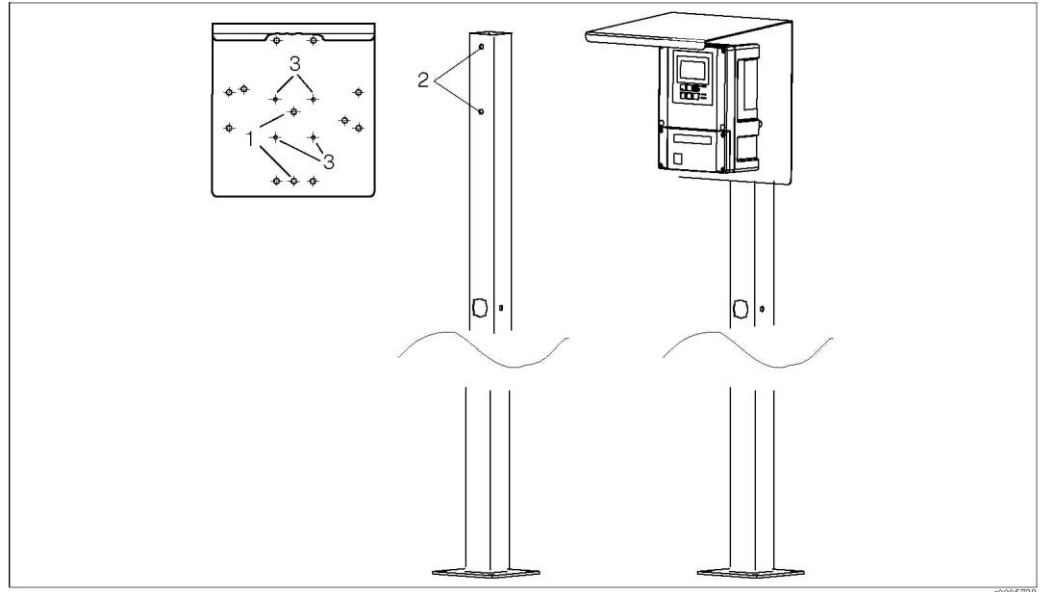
Монтаж полевого прибора на универсальных опорах и установка защитного козырька
